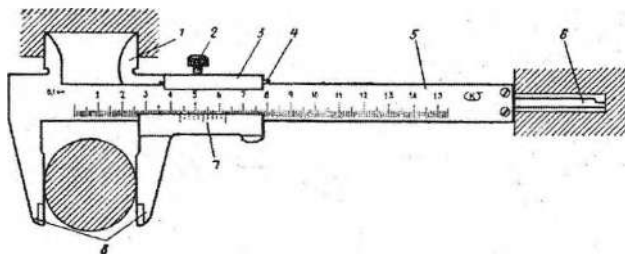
Штангенциркуль ШЦ-I [10, с. 152]
